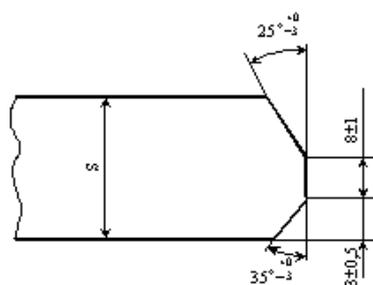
Типы разделки кромок труб диаметром 1020 мм для двусторонней автоматической сварки под флюсом
